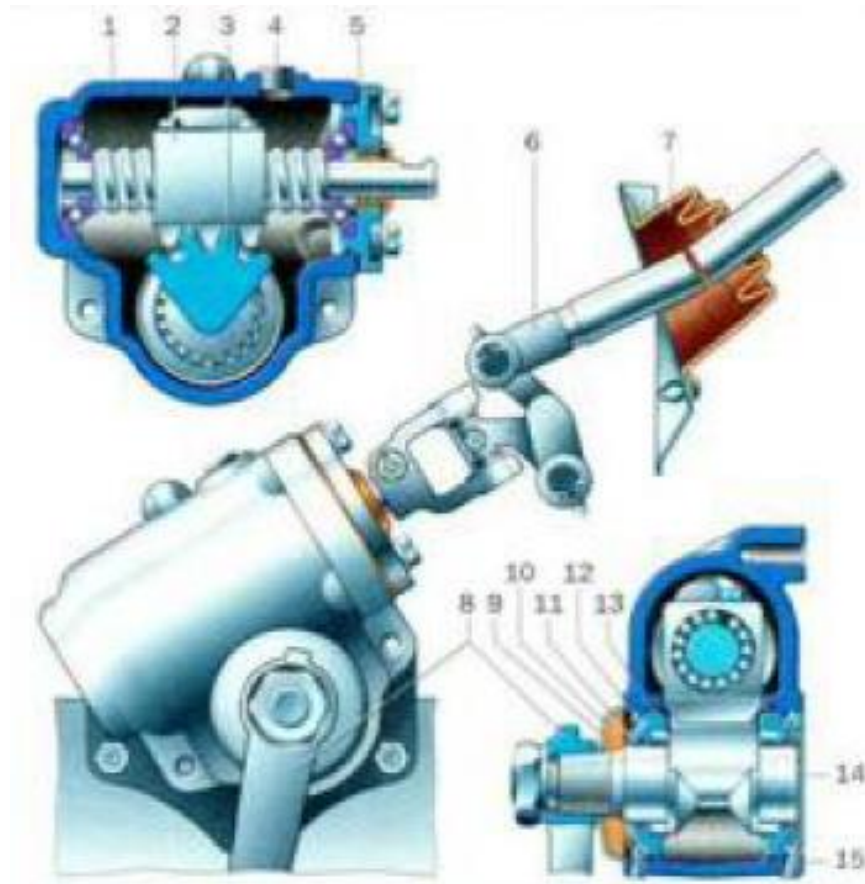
Рульовий механізм типу «гвинт – гайка – рейка – зубчатий сектор» без посилювача: 1 – картерр; 2 – гвинт з кульковою гайкою; 3 – вали-сектор; 4, 15 – пробка; 5 – регулювальні прокладка; 6 – вал; 7, 10 – ущільнювачі; 8 – сошка; 9, 14 – кришки; 11, 12, 13 – кільця
